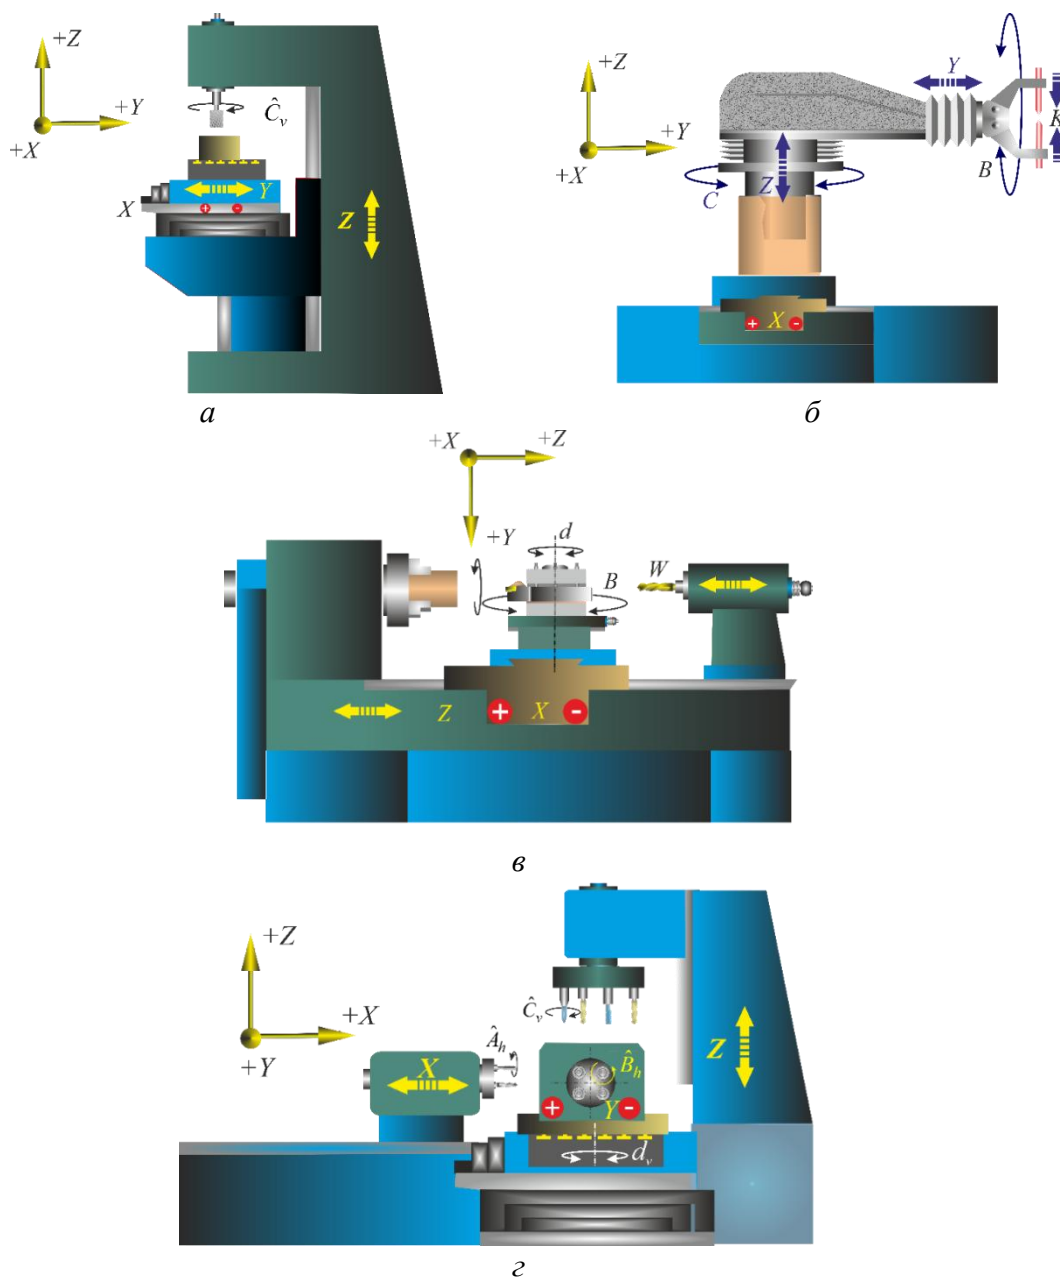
Компоновка технологического оборудования с указанием координатных осей и движений: *a* – фрезерного станка; *б* – промышленного робота; *в* – токарного станка; *г* – агрегатно-сверлильного станка
